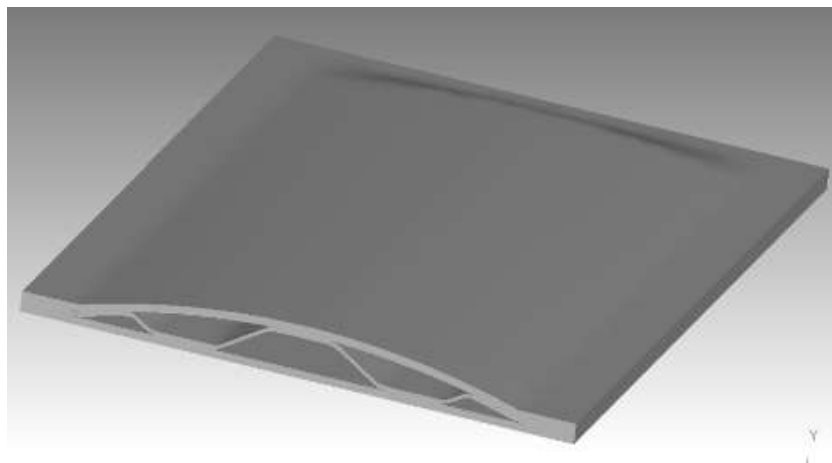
МКЭ - модель трехслойной конструкции в разрезе
